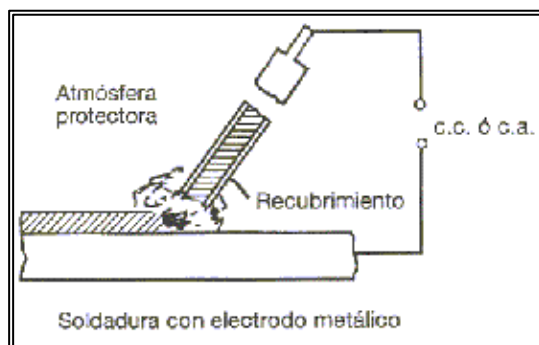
Soldadura al arco con electrodo metálico
